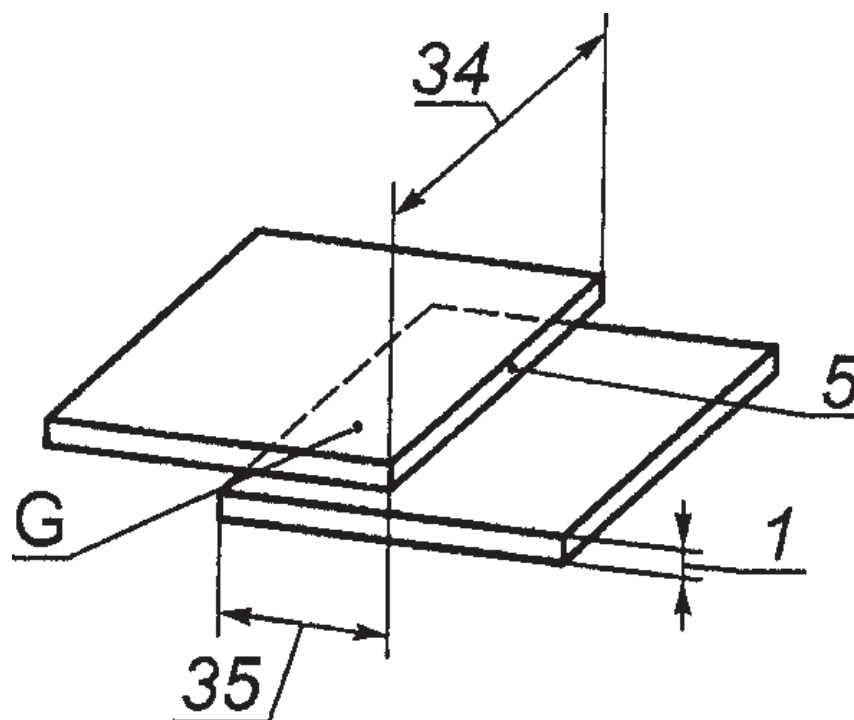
Сборка под контактную точечную и шовную сварки с раздавливанием кромок Figure 10. Configuration for spot,
